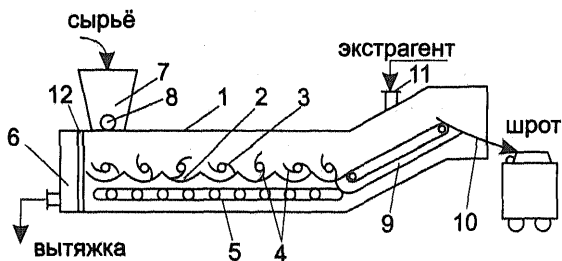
Устройство экстрактора пружинно-лопастного. 1 — корпус; 2 — секции; 3 — барабан; 4 — пружинные лопасти; 5 — камера для обогрева; 6 — камера для сбора извлечения; 7 — бункер для ввода сырья; 8 — дозатор; 9 — транспортёр; 10 — лоток; 11 — сопло подачи извлекателя, 12 — фильтр.
